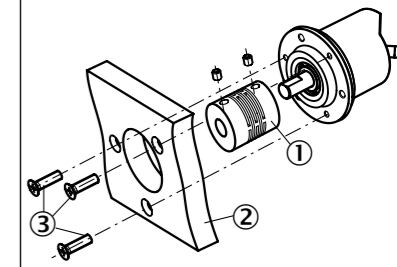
Anbau DBS50 Klemmflansch über flanschseitige Gewindebohrungen
